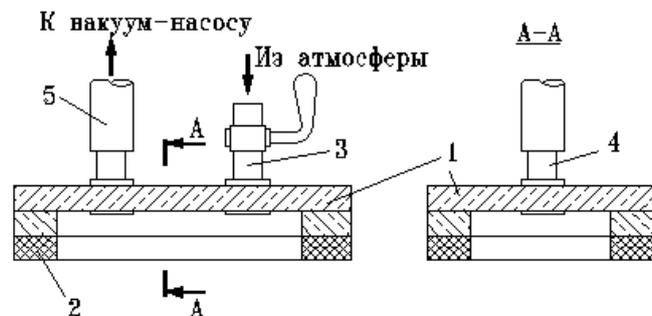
Вакуумная камера плоская для испытания герметичности сварных швов: 1 – корпус из оргстекла; 2 – губчатая резина; 3 – кран; 4 – патрубок; 5 – шланг
